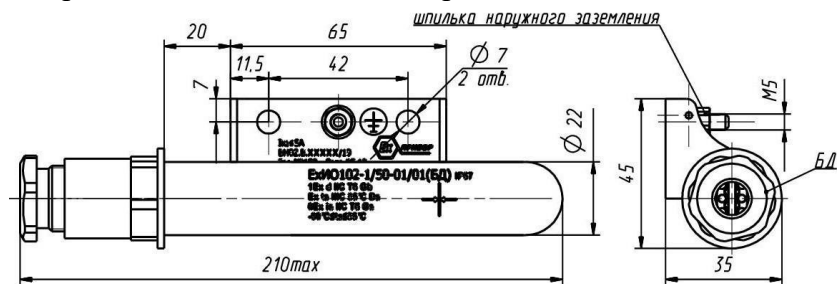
Габаритный чертёж извещателя ЕхИО102-3/50
